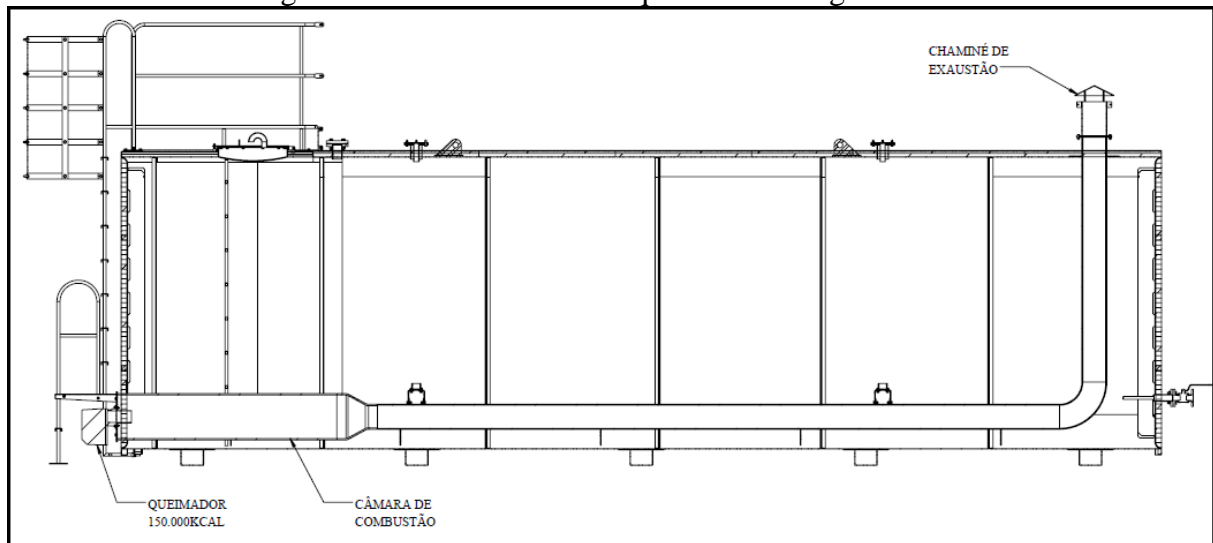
Vista explodida Tanque de CAP Fogo Tubular
